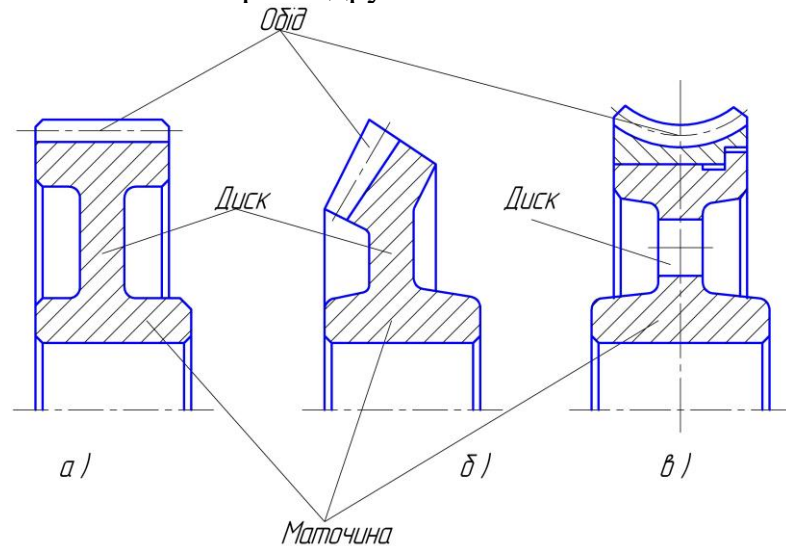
Конструктивні особливості коліс: а – циліндричного; б – конічного; в – черв'ячного
